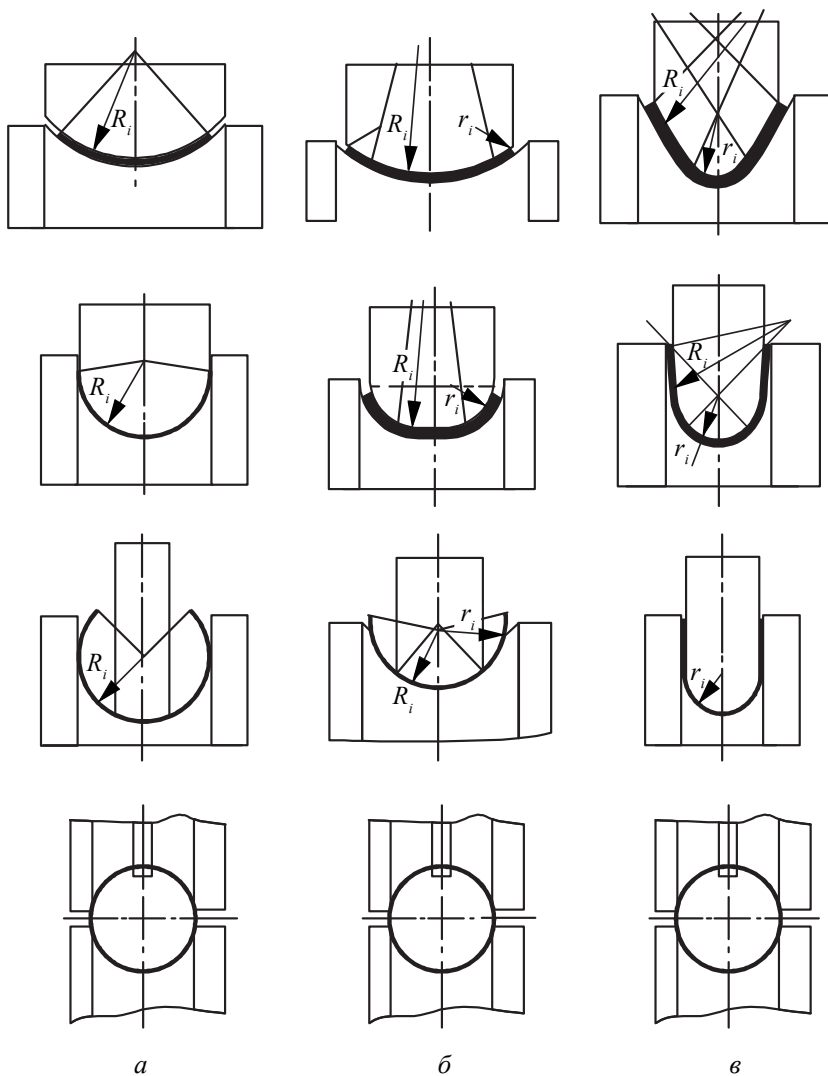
Схемы формовки трубной заготовки на валковых формовочных станах:
